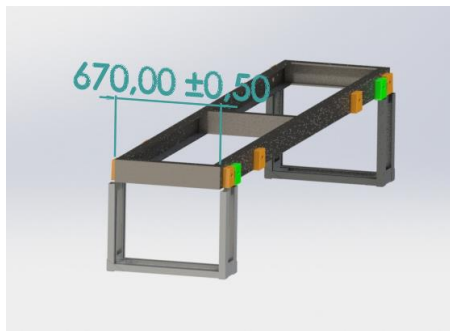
Modelação 3D - CAD com a caixa para os carros de extrusão soldada ao perfil *UPN
